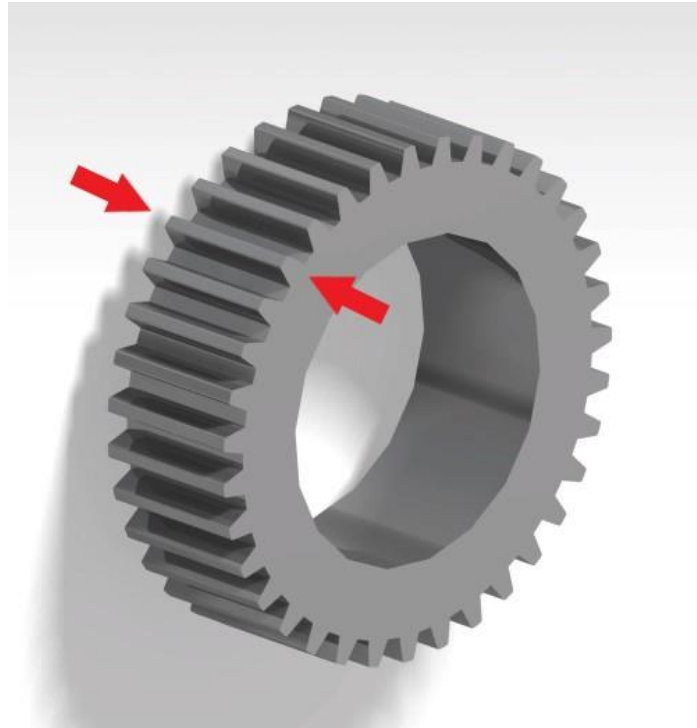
Vista en detalle del ACABADO del engranaje (Fuente: elaboración propia)
